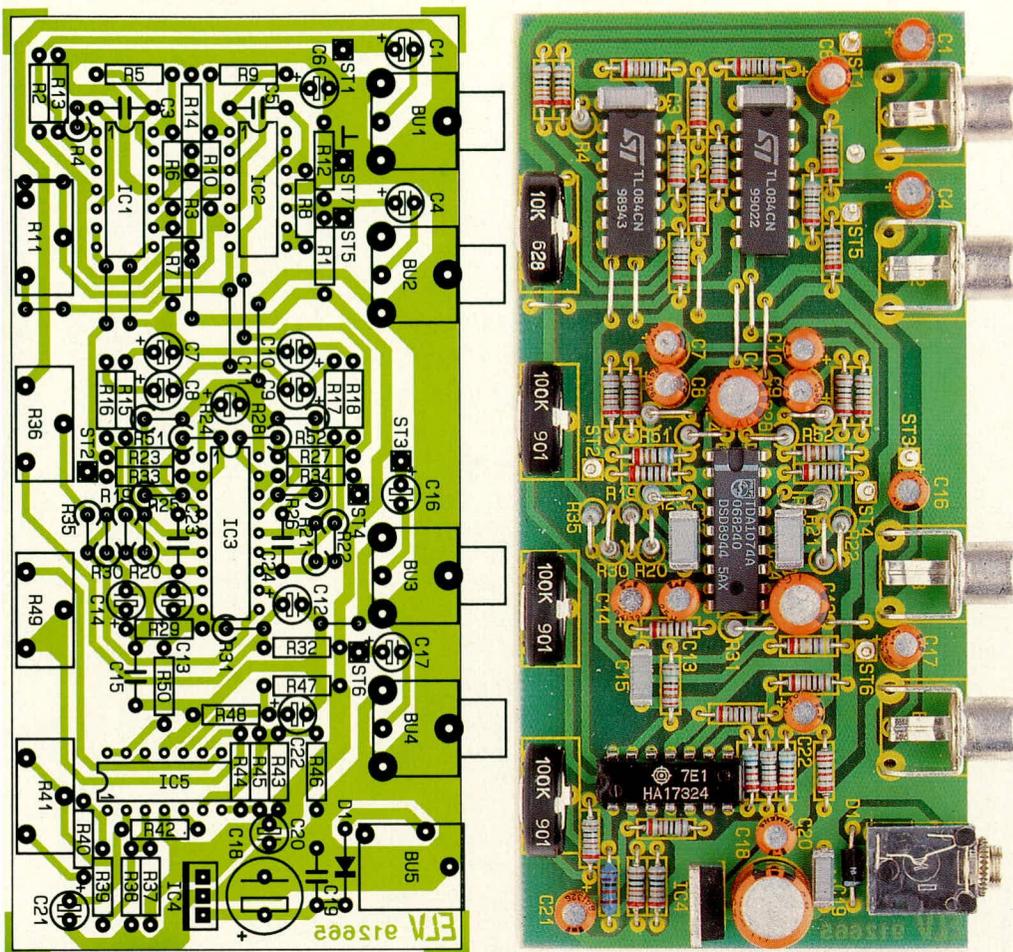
Bestückungsplan und Platinenfoto des fertig aufgebauten FE 1000. Die Leitungen zum Anschluß des Bypass-Schalters sind noch nicht eingezogen.
